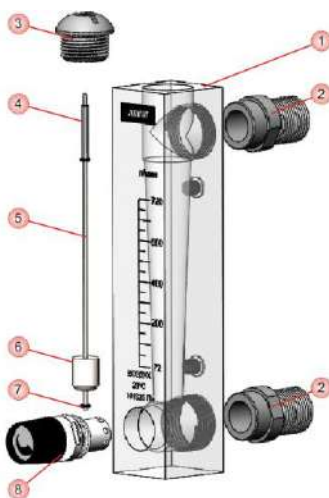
Устройство ЭМИС-МЕТА 211-Р панельный тип (ПА)
